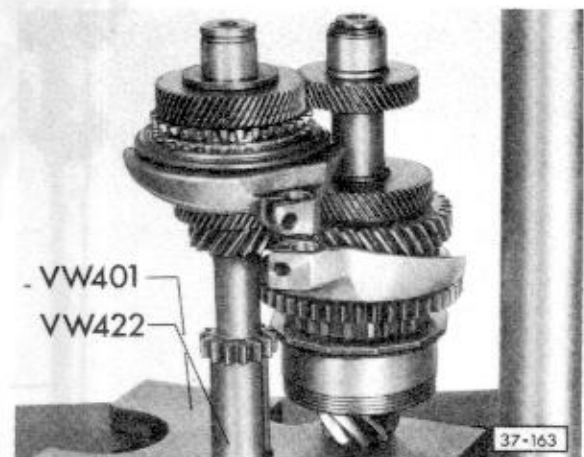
Vor dem Einpressen der Wellen in das Lager-schild Schaltgabel wie gezeigt ausrichten
